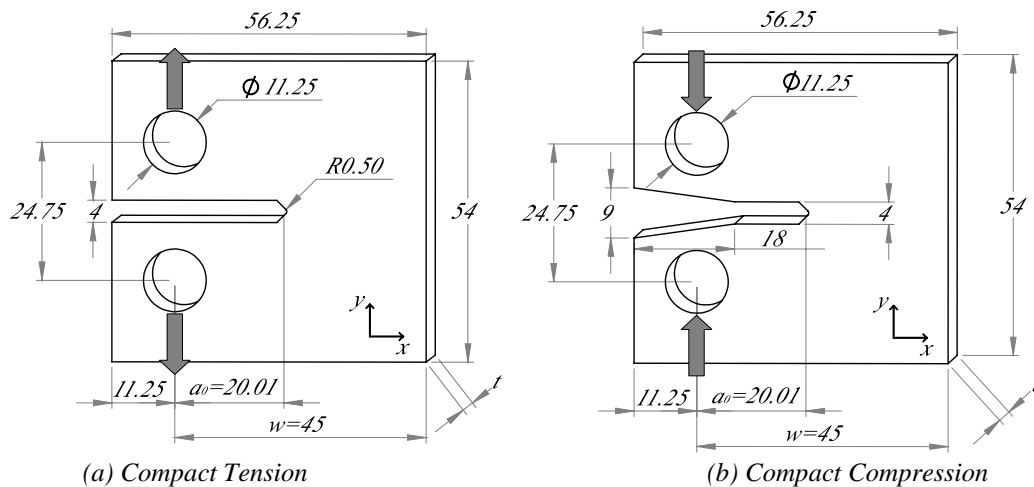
Dimensions des éprouvettes (mm) pour des essais de rupture translatinaire de fibres (a) en traction et (b) en compression
